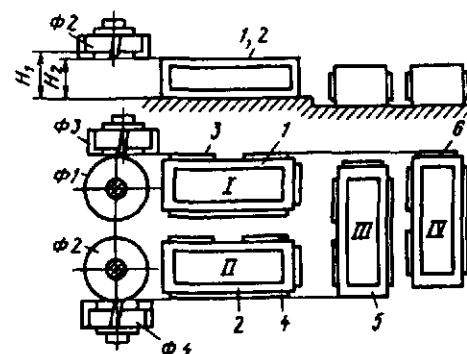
Многоместная многоинструментная параллельно-последовательная схема обработки с перекладыванием заготовок в позициях I – IV
